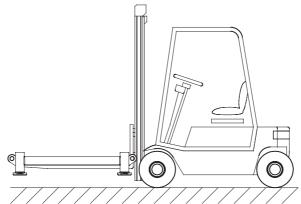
Sollevamento del telaio inferiore con un carrello elevatore.
